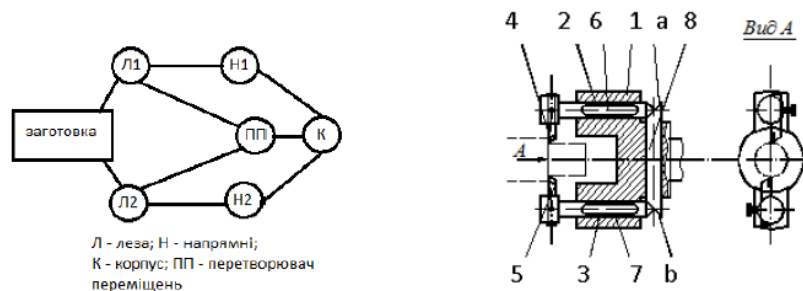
Графовий опис компоновки дворізцевої державки (1 – корпус; 2,3 – пальці; 4,5 – різці; 6,7 – шпоночки з'єднання; 8 – передавальний елемент)
